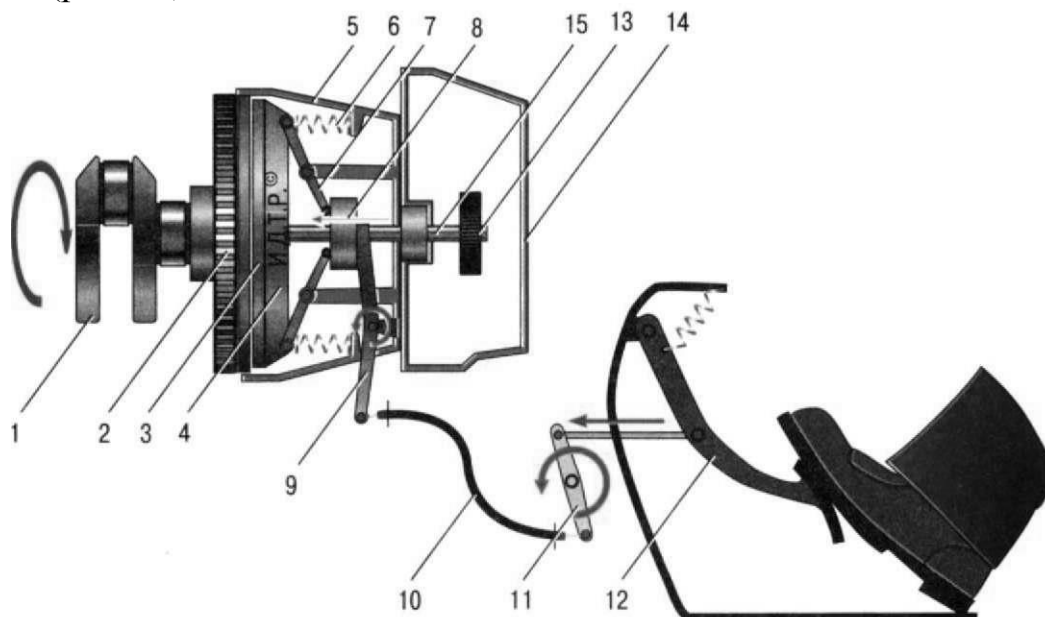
Схема механического привода выключения и механизма сцепления: 1 - коленчатый вал; 2 - маховик; 3 - ведомый диск; 4 - нажимной диск; 5 – кожух сцепления; 6 - нажимные пружины; 7 - отжимные рычаги; 8 - подшипник выключения сцепления; 9 - вилка выключения сцепления; 10 - металлический трос; 11 - рычаг привода; 12 - педаль сцепления; 13 - шестерня первичного вала; 14 – картер коробки передач; 15 - первичный вал коробки передач
